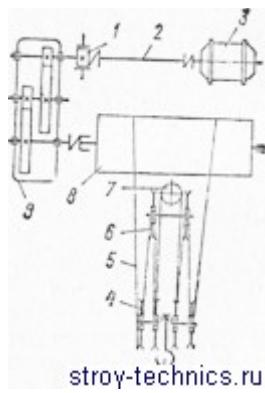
Схема механизма подъема с приводом от электродвигателя
